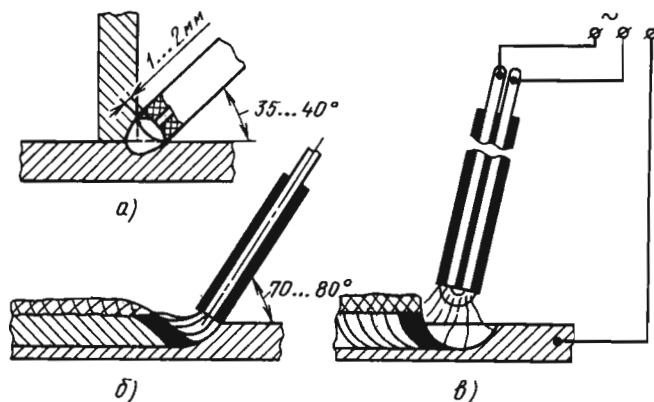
Схемы сварки с глубоким изготовлением угловых (а) и стыковых швов (б) и сварки трехфазной дугой (в)
